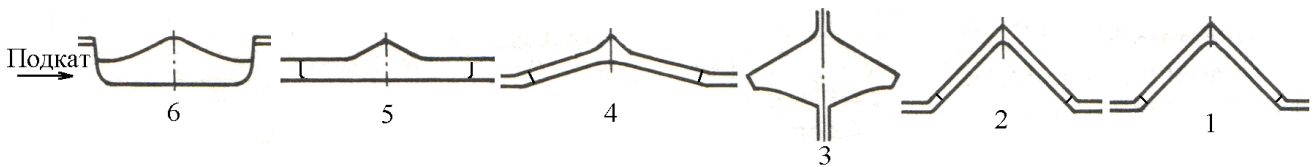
Принципиальная схема прокатки угловой стали на стане 320/150 (1-6 – номера калибров против направления прокатки)
